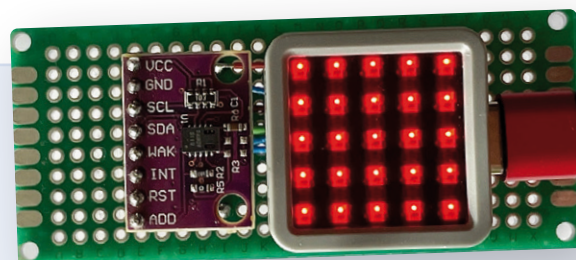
Soudure facile des deux modules sur la carte perforée.
